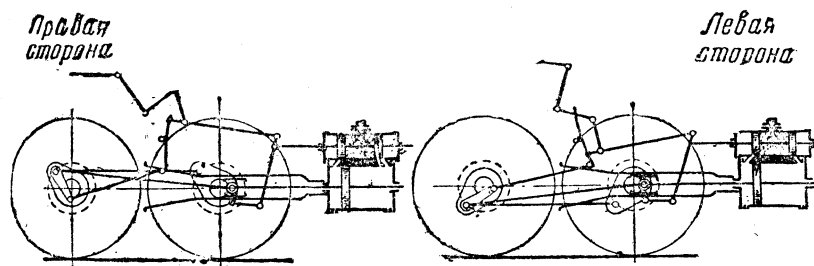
Установка машины паровоза для проверки плотности поршневых и золотниковых колец
